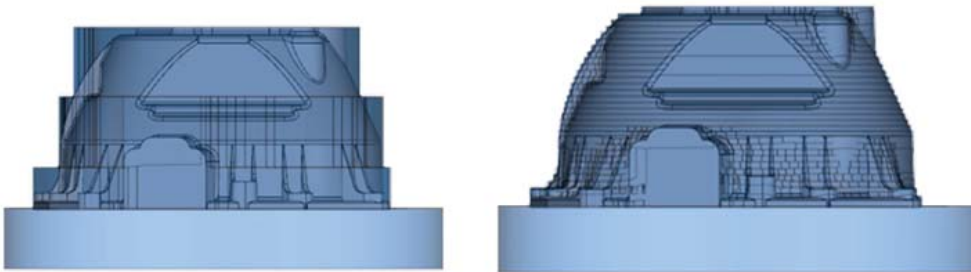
Конечная заготовка без применения и с применением стратегии черновой обработки "Сверху–Вниз"
